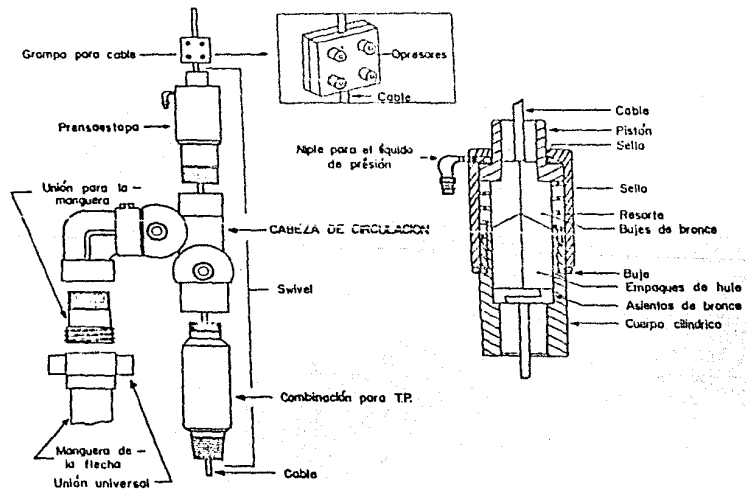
ENSAMBLE DEL PREÑAESTOPA
